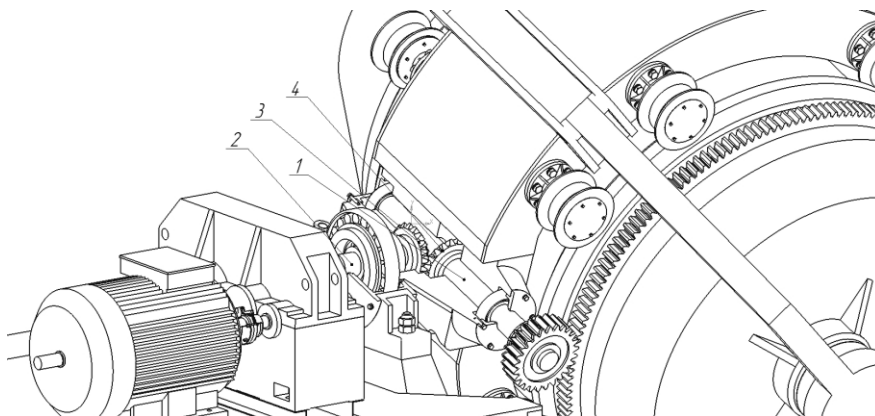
Предложенная конструкция механизма вращения корпуса
